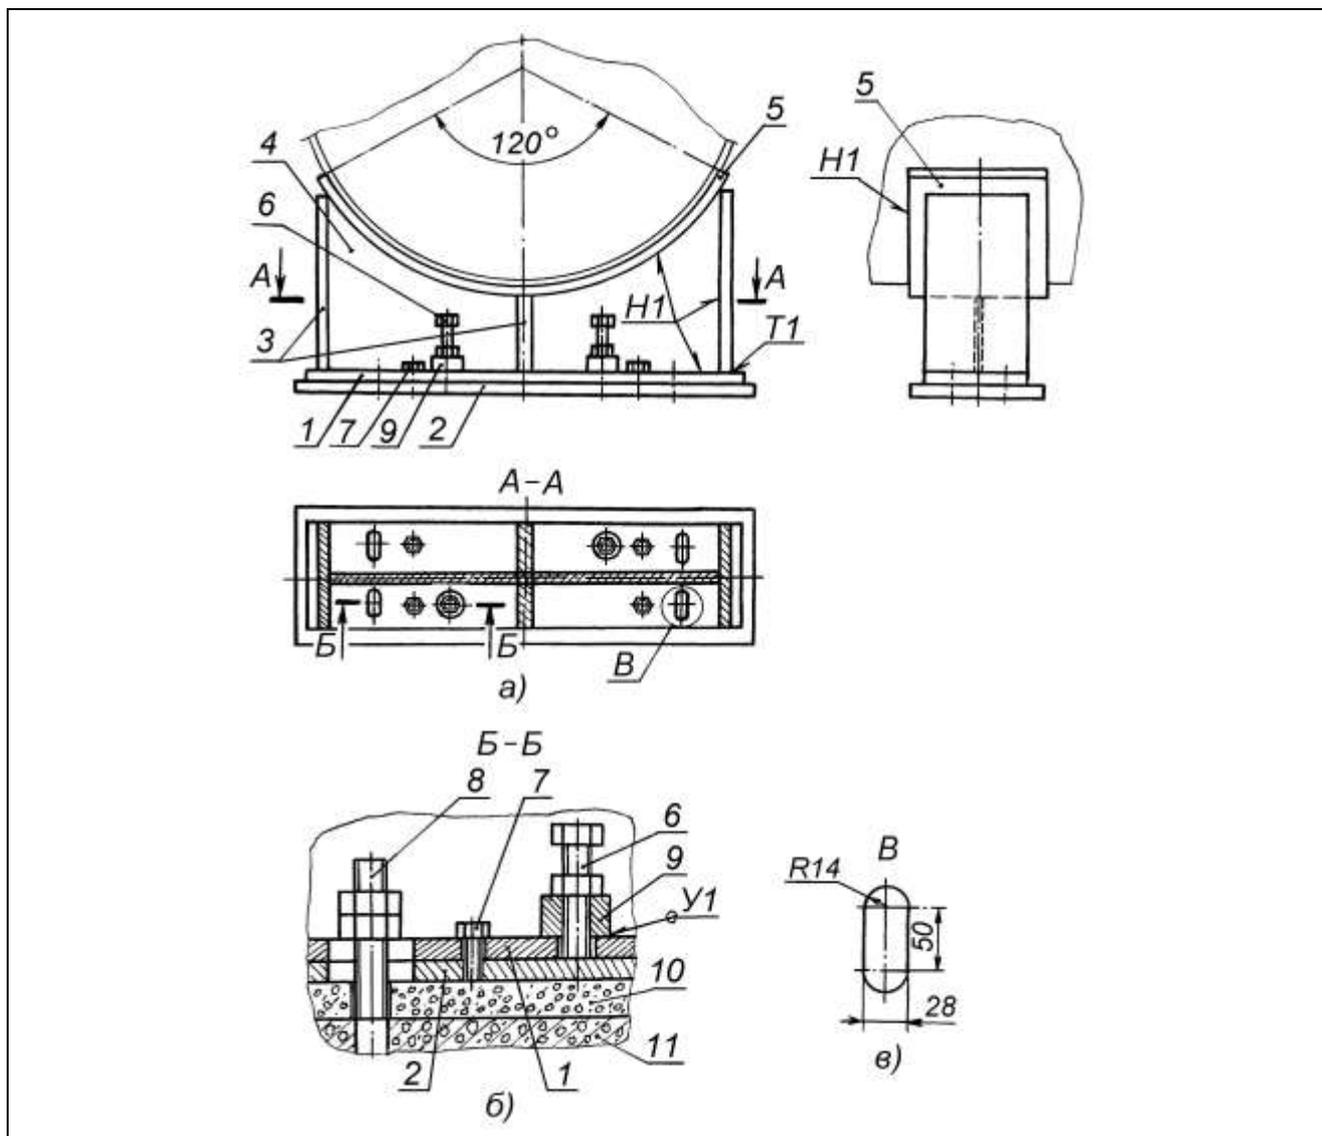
Опора седловая подвижная (тип 2) для горизонтальных теплообменников: а) – общий вид; б) – схема установки опоры на фундаменте 11; в) – форма и размеры отверстия под фундаментный болт
